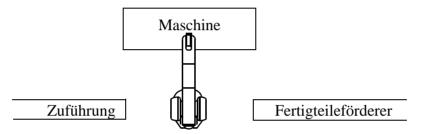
Der Manipulator beschickt eine Maschine, die das Werkstück bearbeitet.
